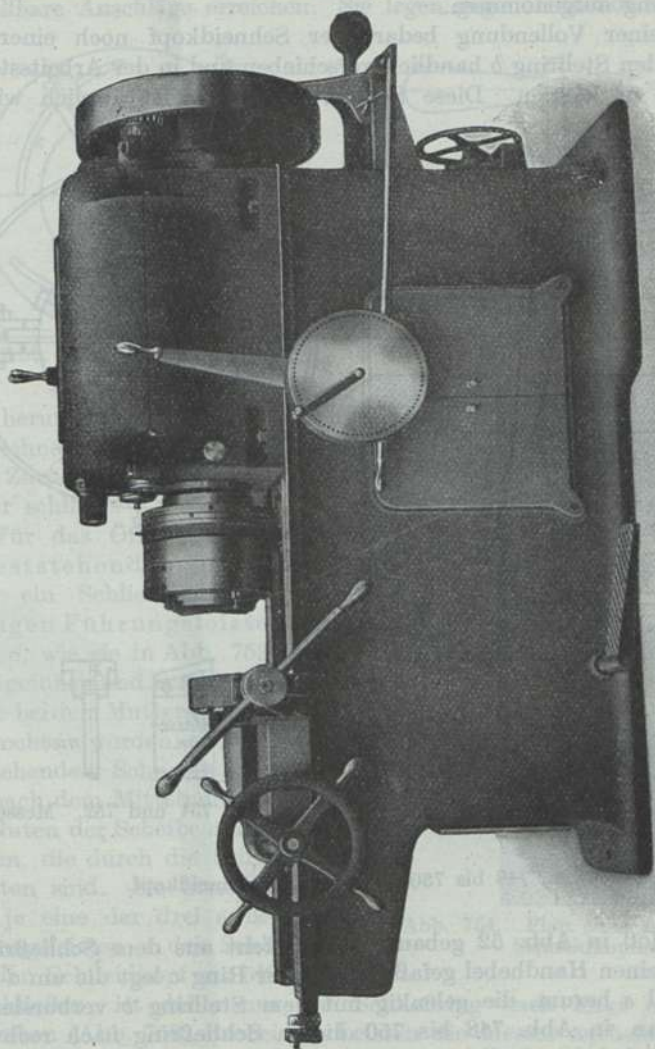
Selbsttätige Gewindeschneidmaschine mit Stufenraderantrieb für 10 Geschwindigkeiten.
